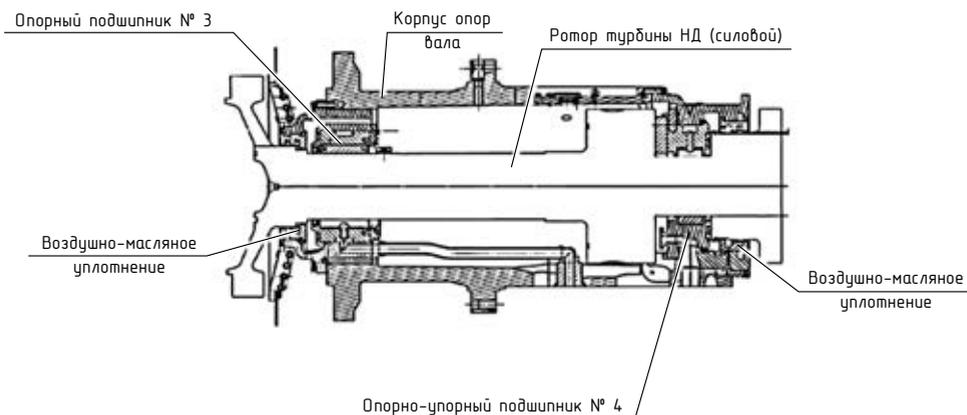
Корпус опор вала ТНД (силовой)
